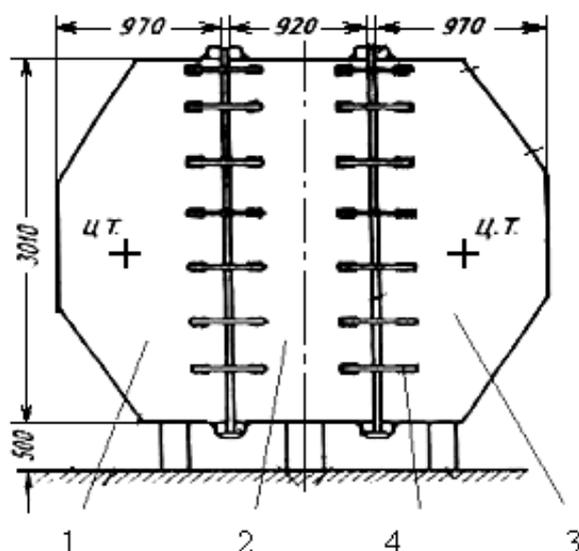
Схема установки днища на опоры под сварку:
